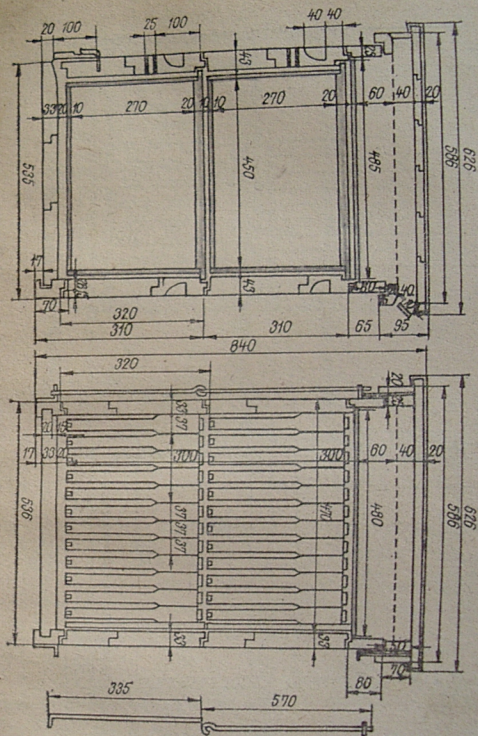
Secțiune longitudinală și transversală în stupul vertical cu două corpuri
